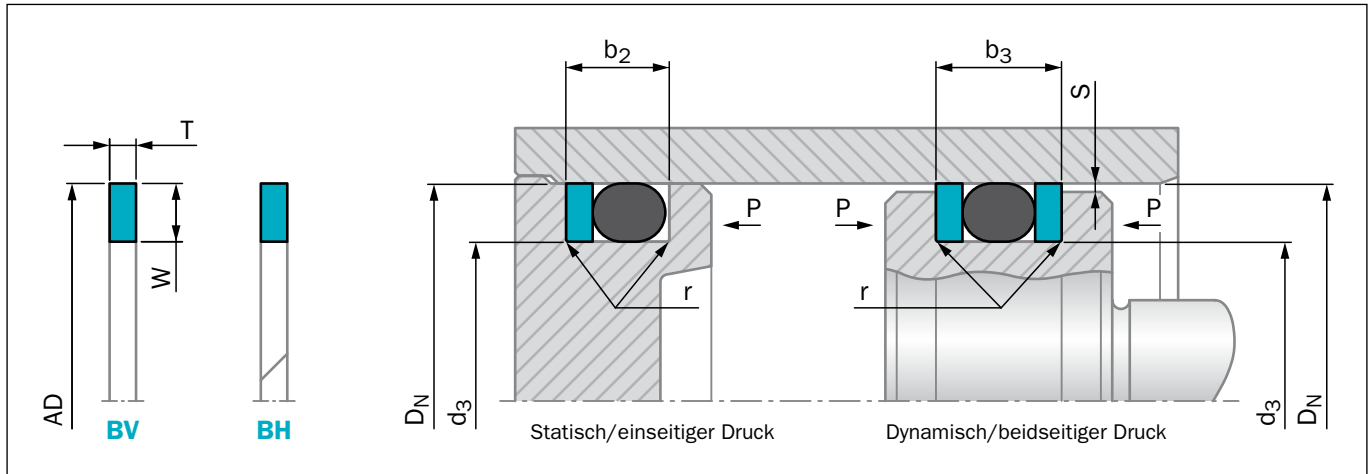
Einbauzeichnung außendichtend, rechteckige Stützring-Typen
